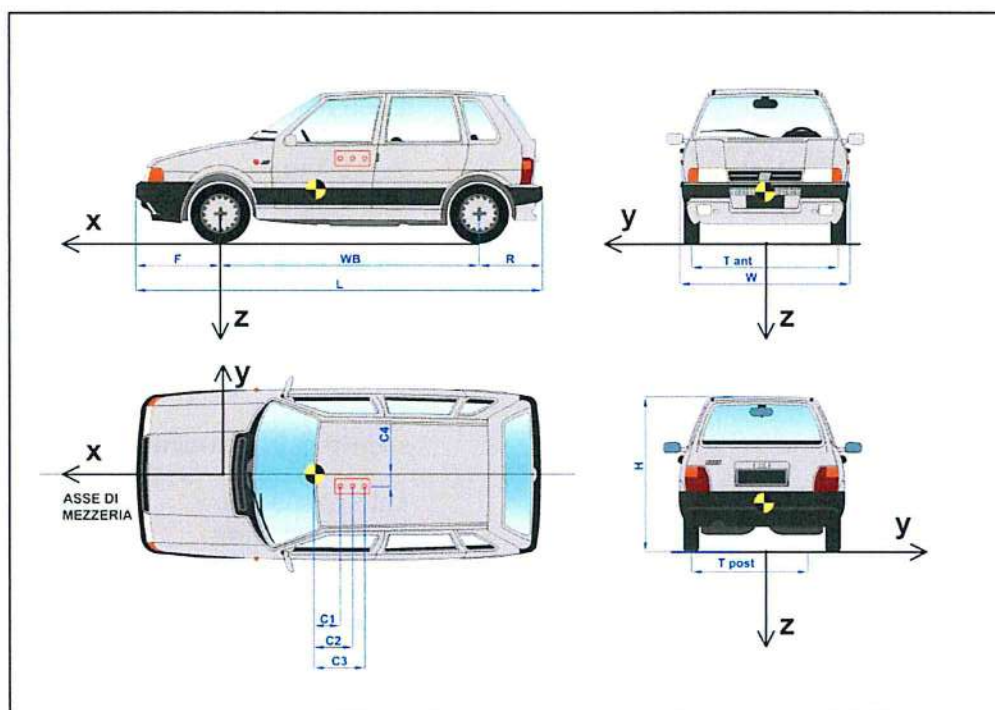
Dimensioni del veicolo – Vehicle dimensions
